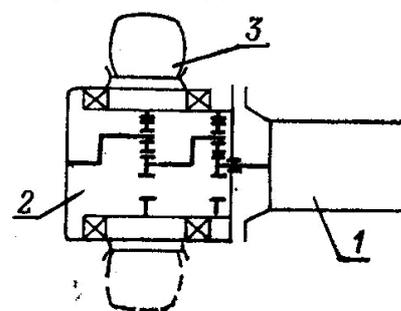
Структурна схема мотор-колесного тягового привода: 1 - ТЕД; 2 - планетарний редуктор; 3 - колесо
